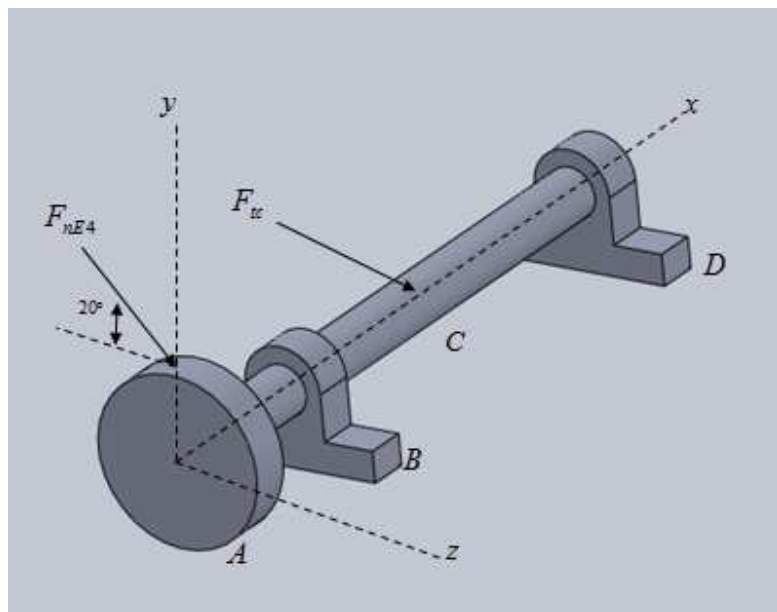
Disposición del engrane 4 sobre el eje 4.
